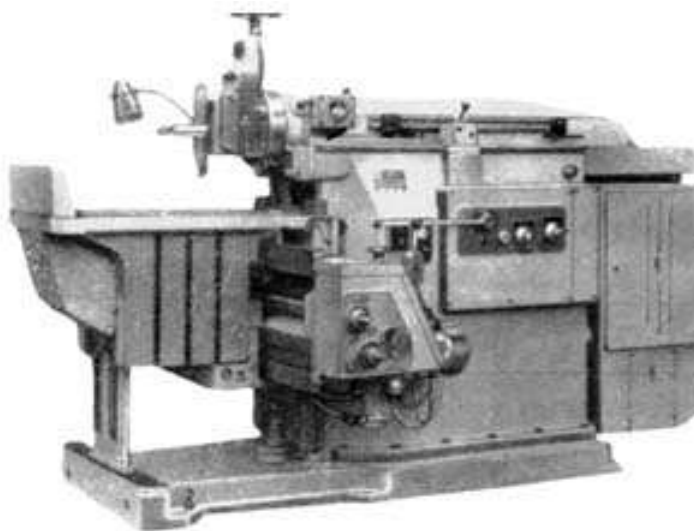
Поперечно-стругальний верстат 7Д36 [12]
